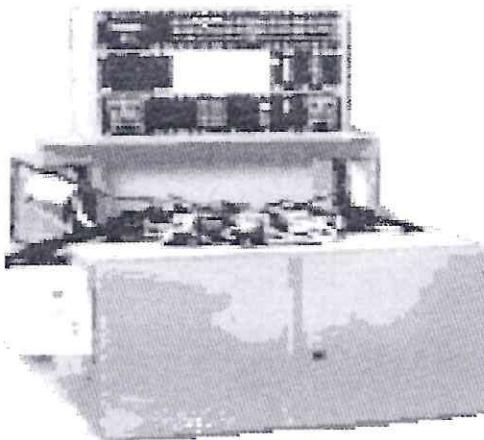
Прибор для контроля крестовины карданного вала БП-1.
